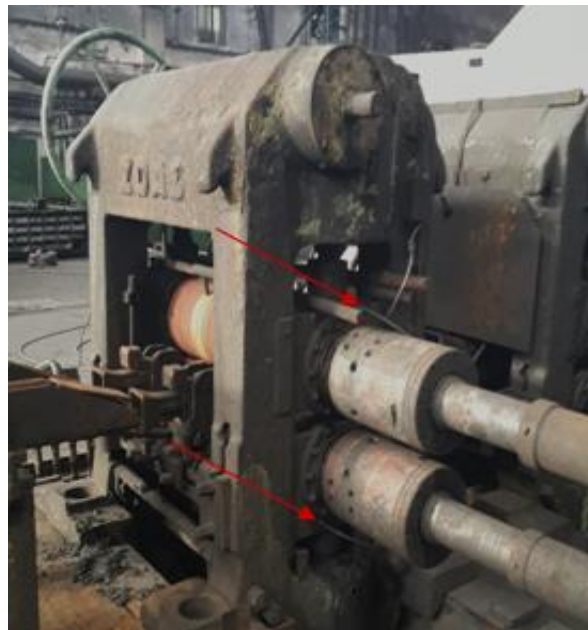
Detail potrubních rozvodů, rozdělovače na zadní straně válcovací stolice a 2 MB [autor]
